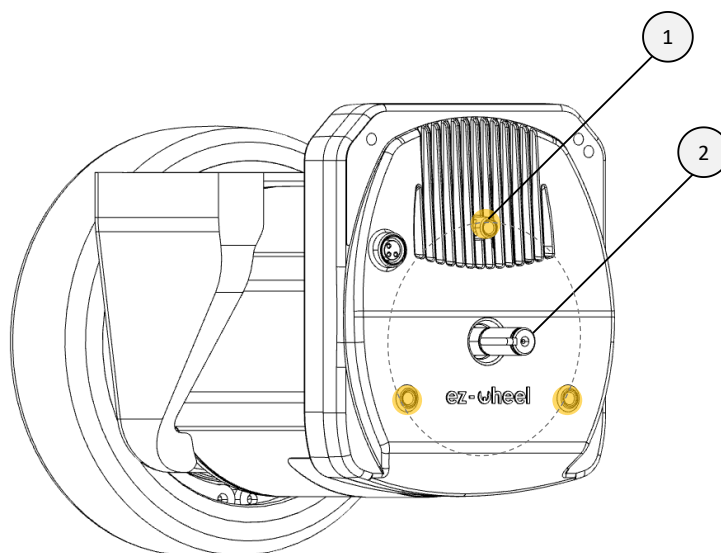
Vue d'ensemble des interfaces mécaniques – SWD® 125
